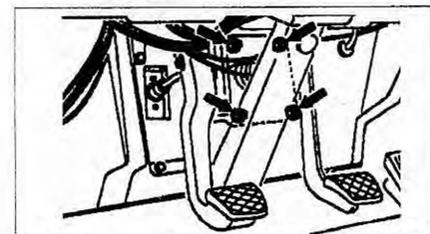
Снимите вакуумный усилитель тормозного привода. При установке используйте только новые болты крепления.
